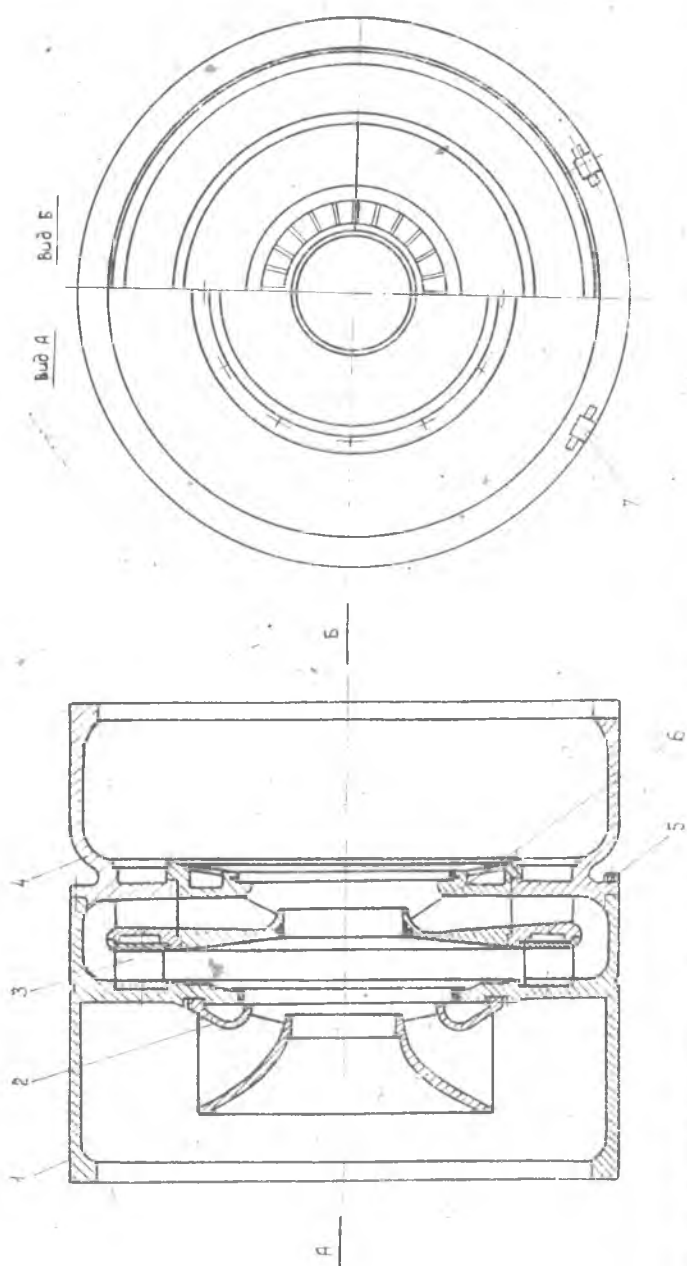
Корпус внутренних: 1 — камера газоприемная; 2 — аппарат входной направляющий; 3 — диффузор лопаточный; 4 — диафрагма; 5 — болт; 6 — аппарат обратный направляющий; 7 — ротор.
